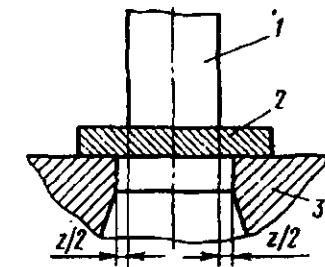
Схема вырубке (пробивки): 1 — пуансон; 2 — заготовка; 3 — матрица; z — зазор
